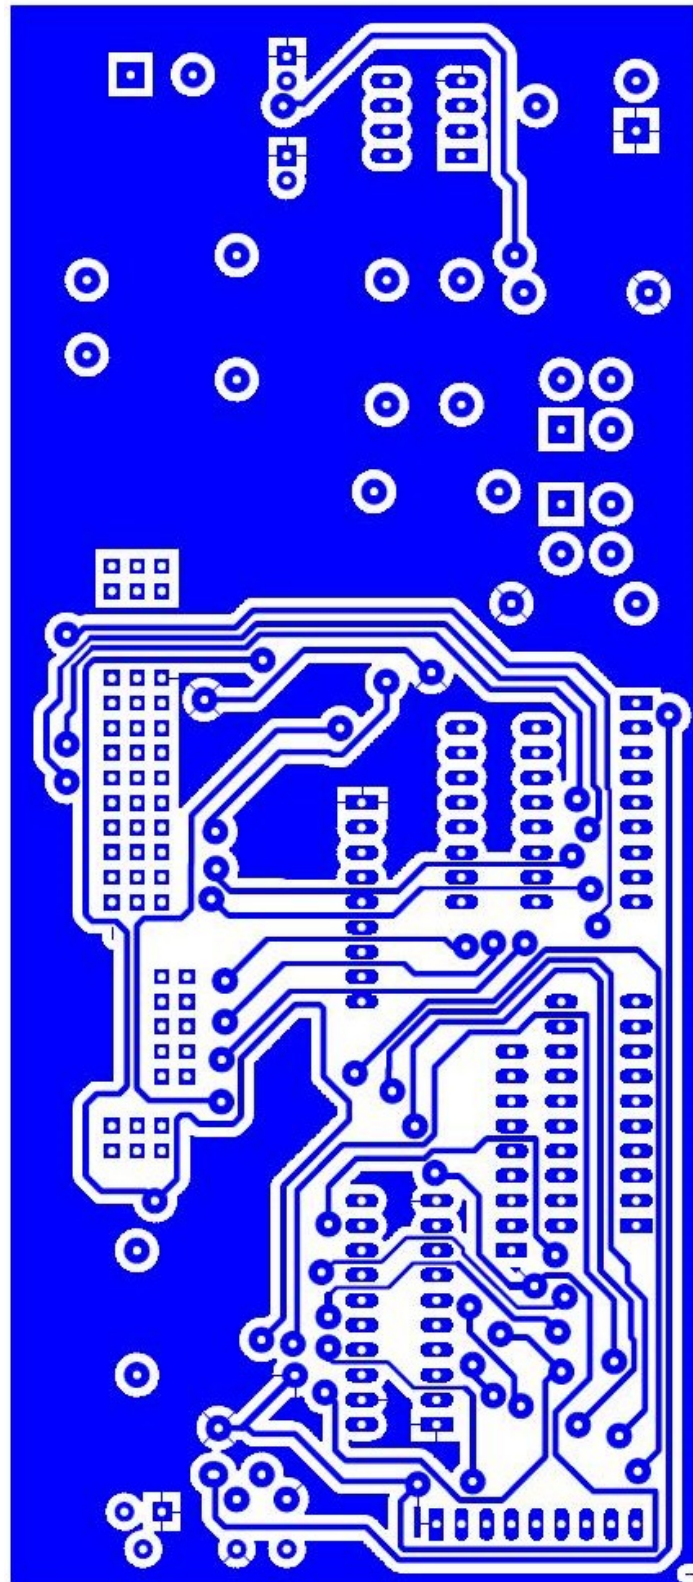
Trazado de las pistas en la cara superior del PCB.
